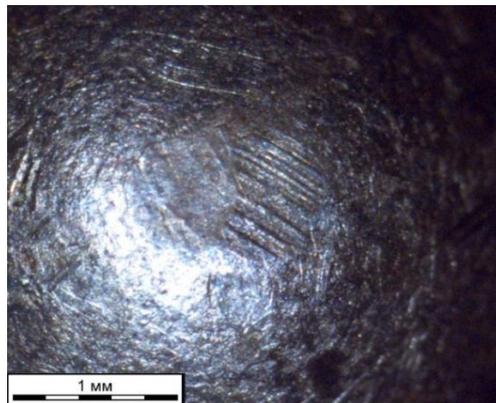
Динамический след посадочного конуса на вершинке пули патрона 7,62 × 25
